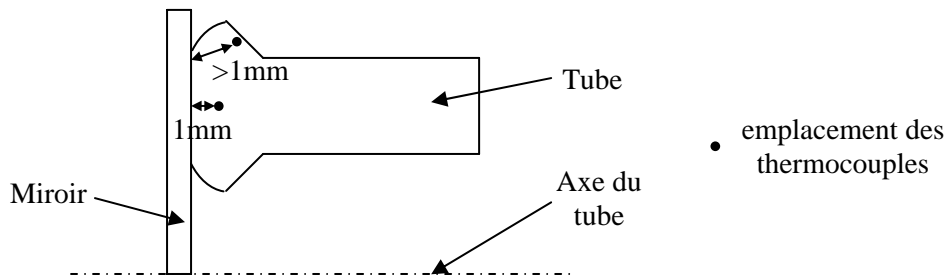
Position en fin de chauffage des thermocouples placés initialement à 1 mm du plan de soudage au centre de la paroi et à 1 mm sous la surface du tube
